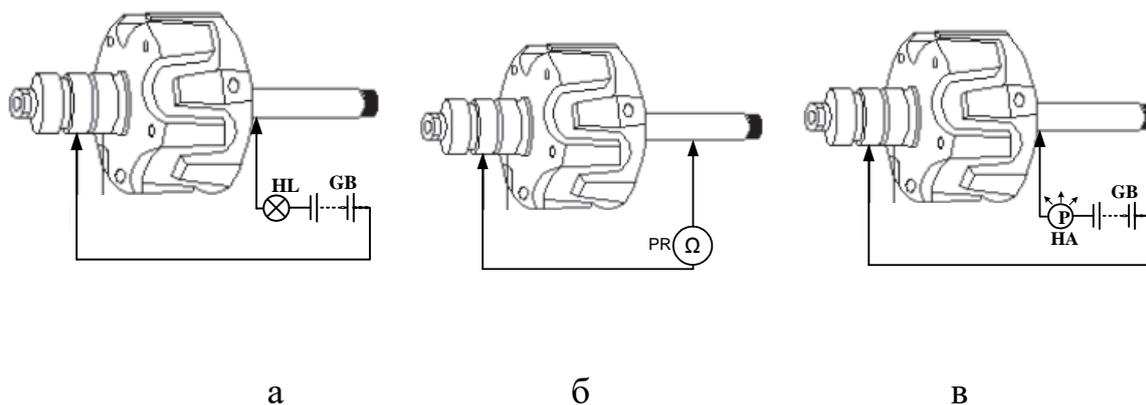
Схема проверки обмотки возбуждения с корпусом ротора.
